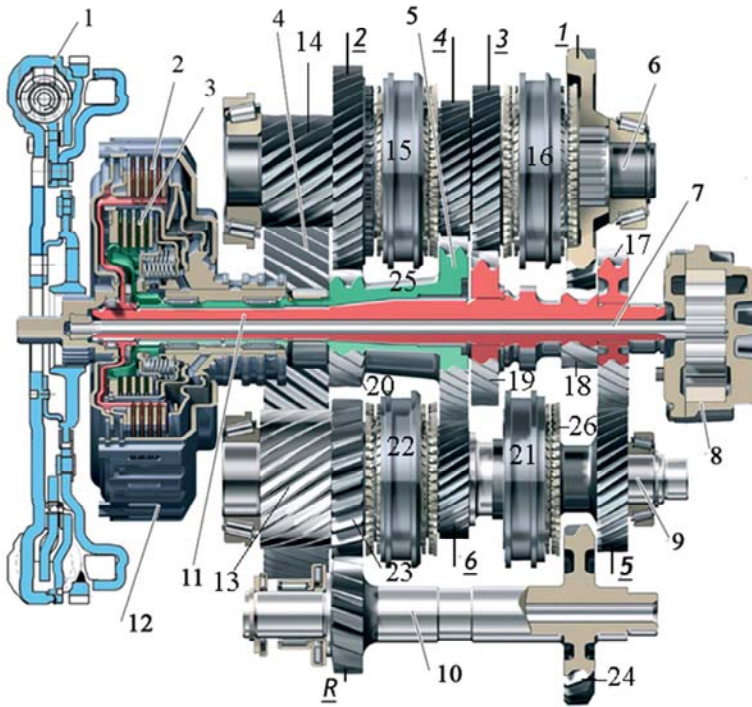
Схема коробки передач с двойным сцеплением:
